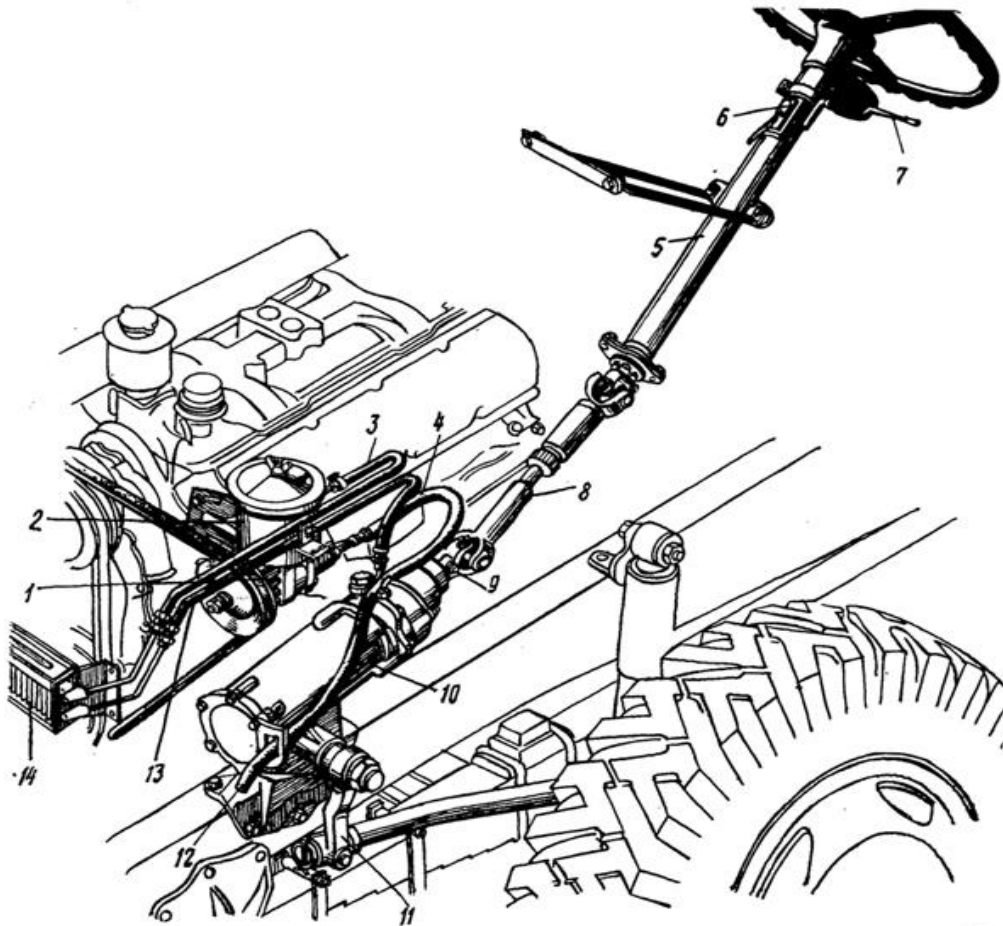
Общий вид рулевого механизма автомобиля:
